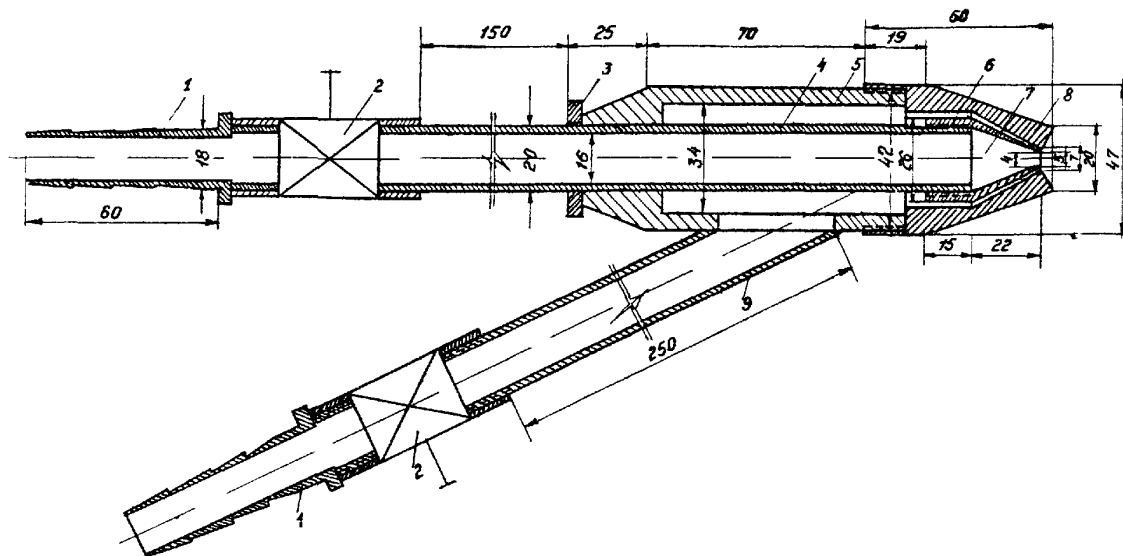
Схема распылительной форсунки: 1- штуцер; 2- пробковый кран; 3- контргайка; 4- втулка; 5- основание; 6- насадка; 7- смесительная камера; 8- головка; 9- патрубок (размеры в миллиметрах).
